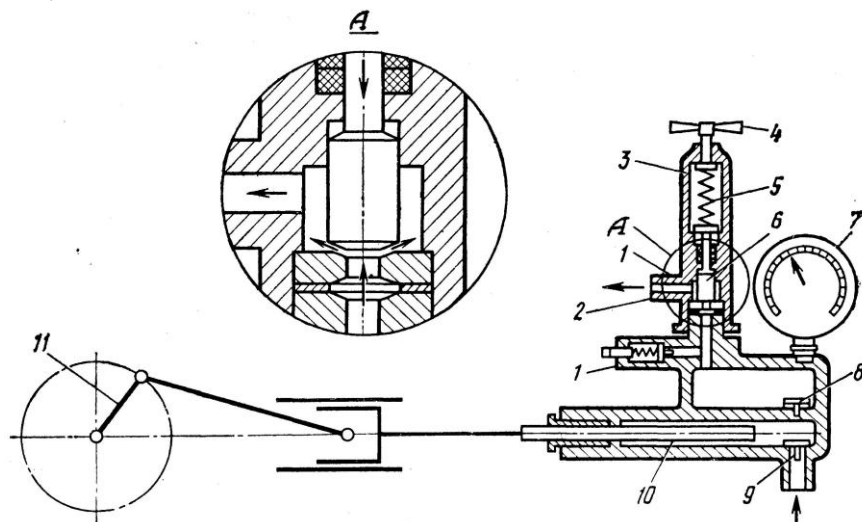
Схема гомогенізатора клапанного типу: 1-запобіжний клапан; 2-вихідний патрубок; 3- корпус; 4- гвинт; 5- пружина; 6- клапан гомогенізуючої головки; 7- манометр; 8- нагнітальний клапан; 9- всмоктуючий клапан; 10- плунжер; 11- привідний механізм.
